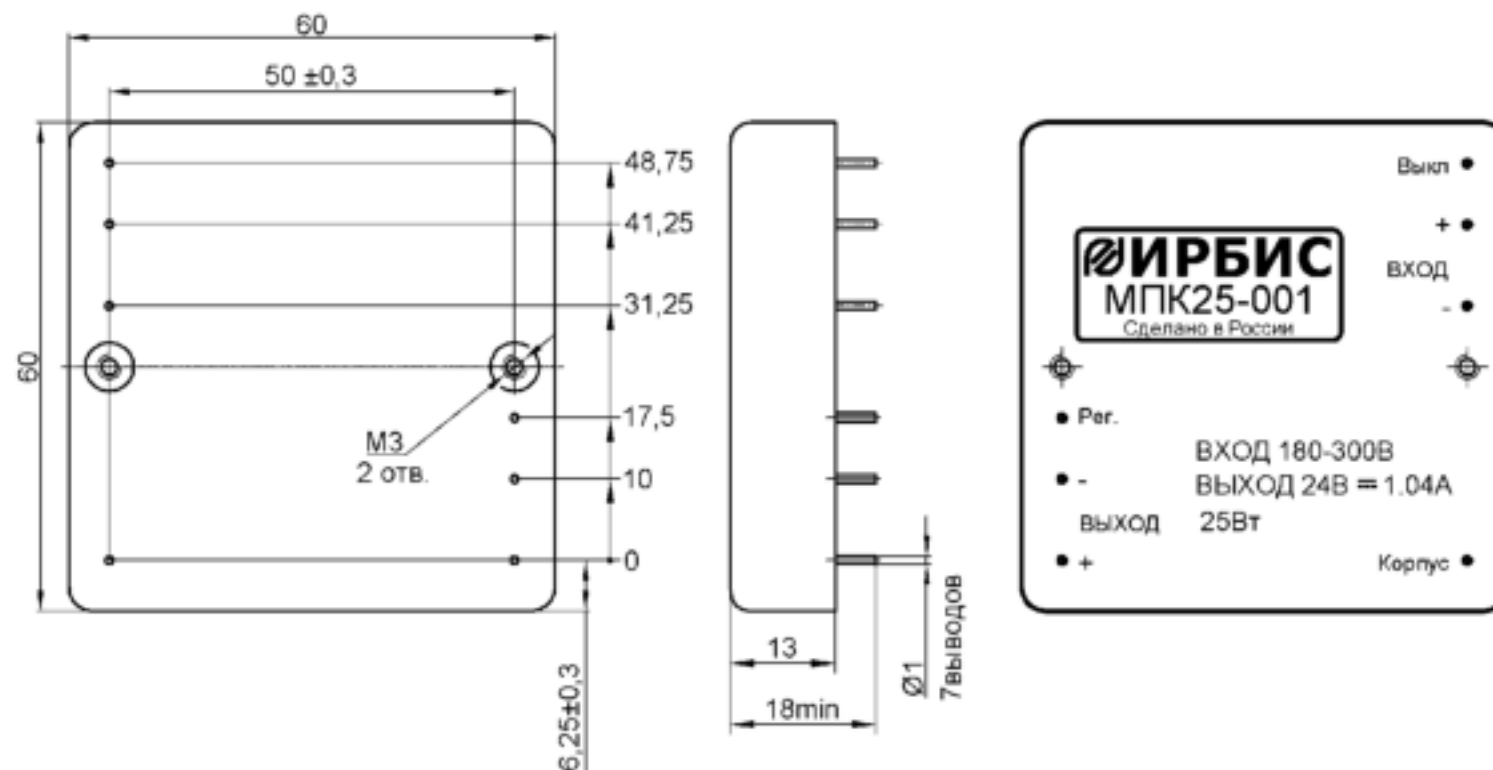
Габаритный чертеж модулей МПК25-001
